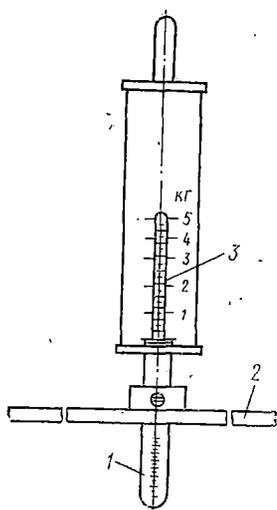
Приспособление для проверки натяжения ремня вентилятора:
